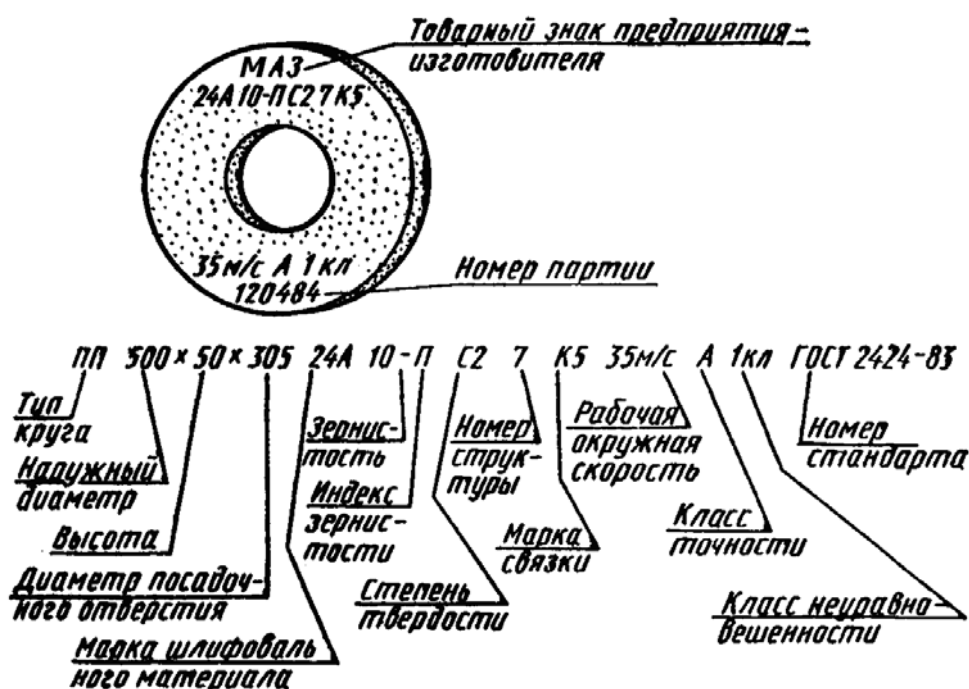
Маркировка и условное обозначение абразивного дискового инструмента
